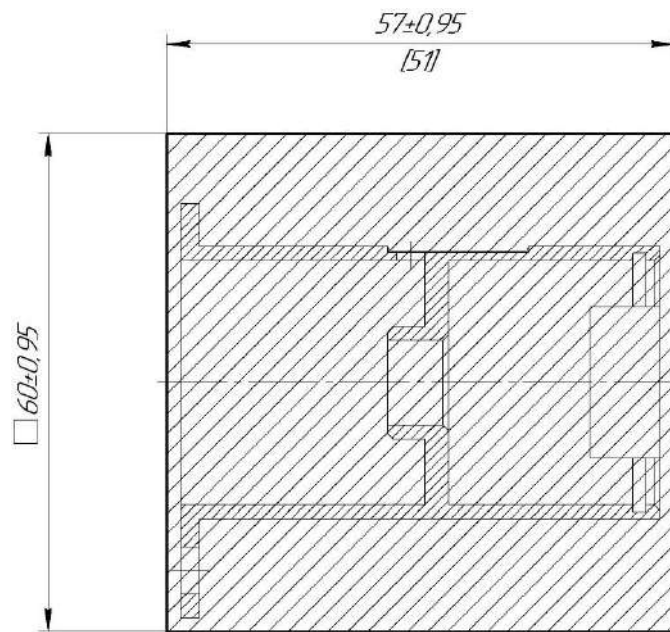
Креслення заготовки отриманої з каліброваного прокату
